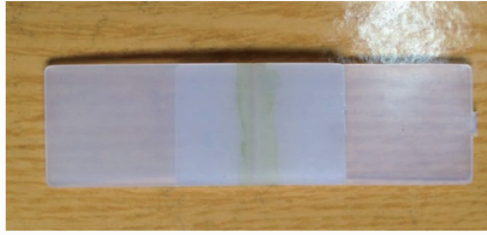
接枝改性聚丙烯与尼龙 66 焊接件
